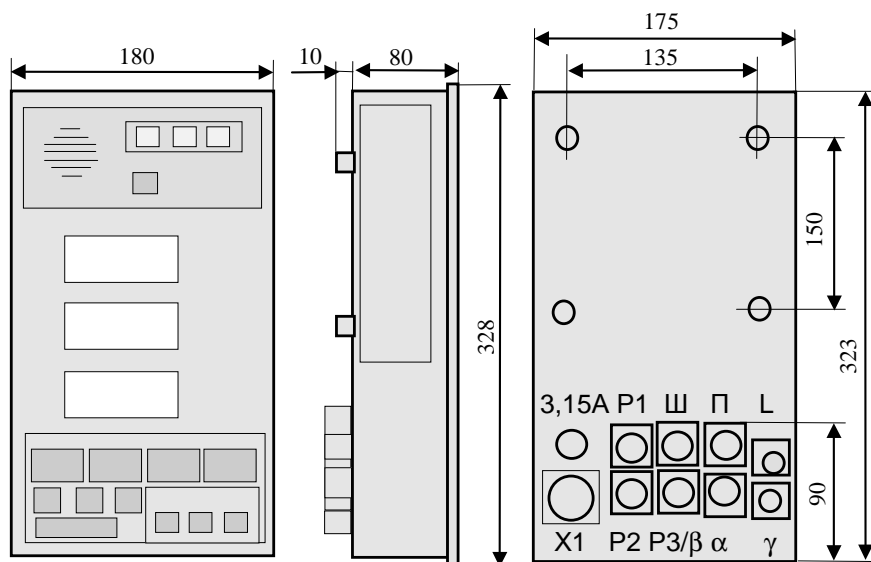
Габаритные и присоединительные размеры БОДа
